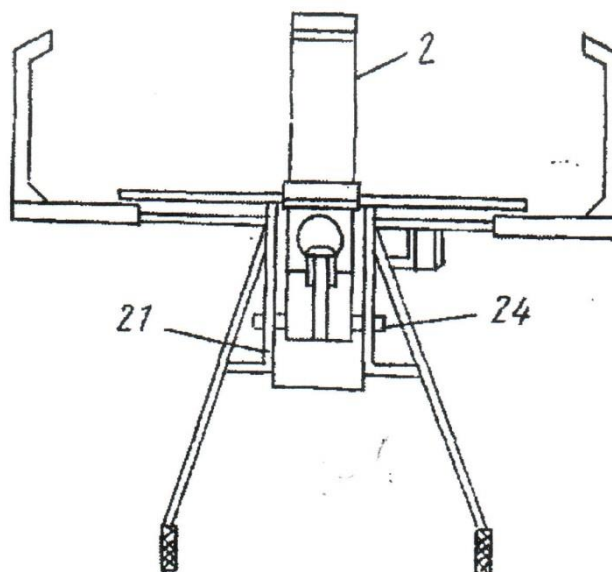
Пристрій для заміни коліс транспортного засобу (вид зверху)
